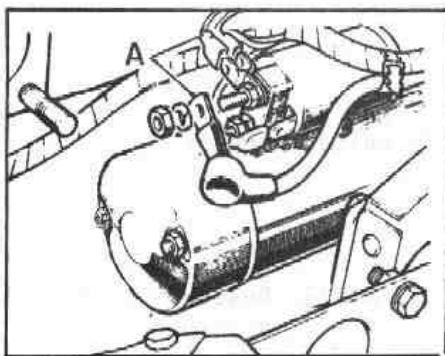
Desmontaje de los cables de alimentación del motor de arranque
